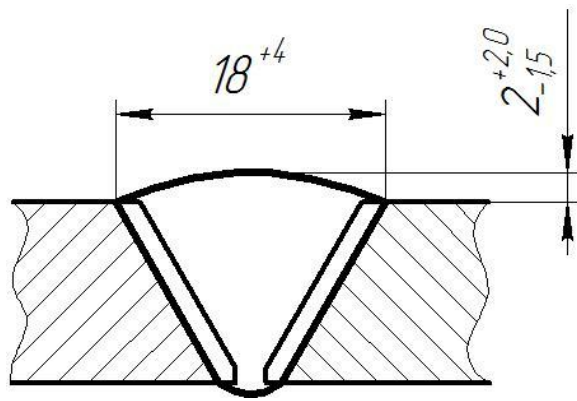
Конструктивные элементы сварного шва
